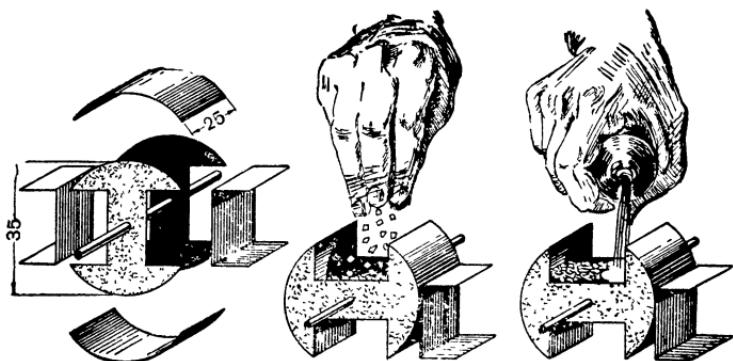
Набивной двухполюсный якорь. Внизу слева — заготовка стенки паза; справа — щека.
